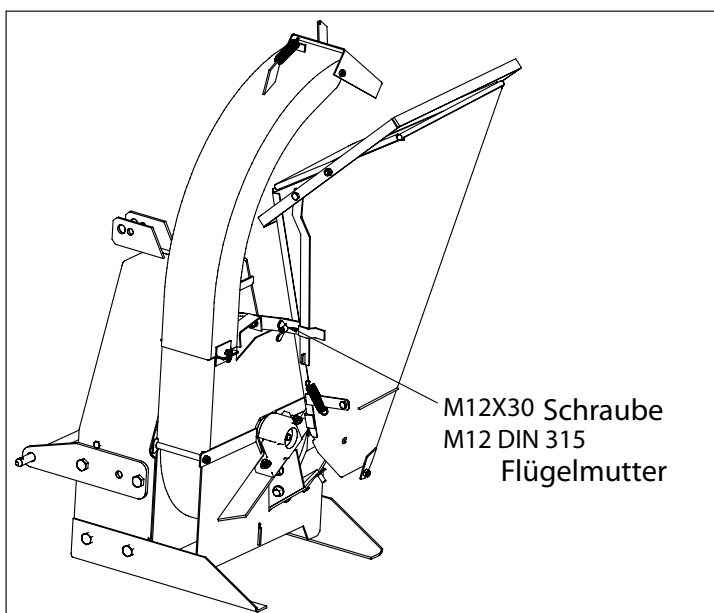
Schwenken des Zuführtrichters in die Transportposition
